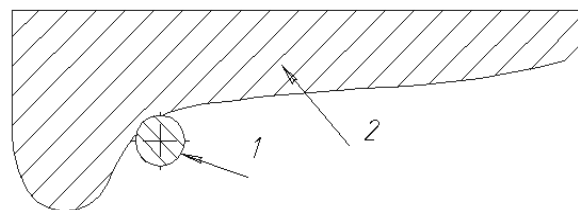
Чашечный резец, работающий в зоне выкружки на поверхности профиля колеса
